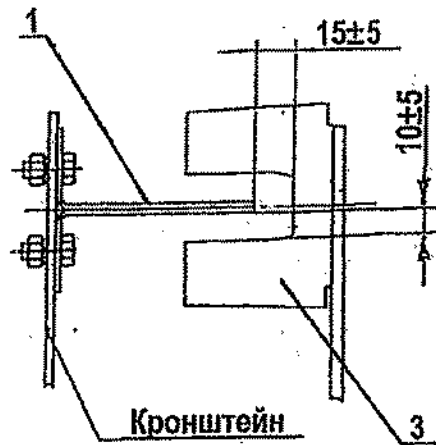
схемы сборки натяжного устройства каната ОС
